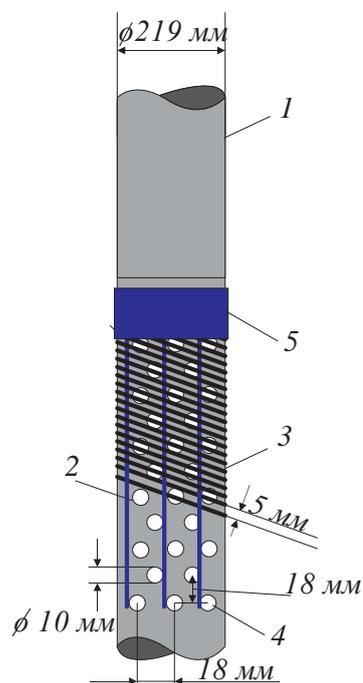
Схема расположения отверстий для изготовления фильтра
